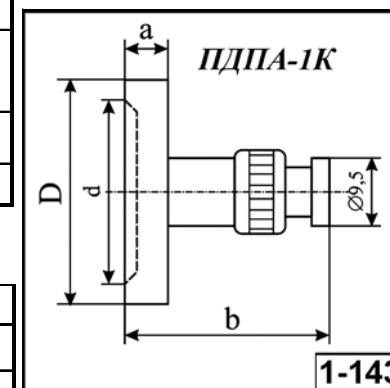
Внешний вид и габаритные размеры детекторов типа ПДПА-1К
